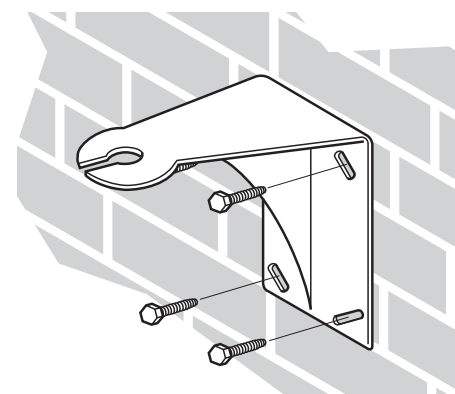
Fissaggio della staffa di montaggio LBB 3414/00 ad una parete
